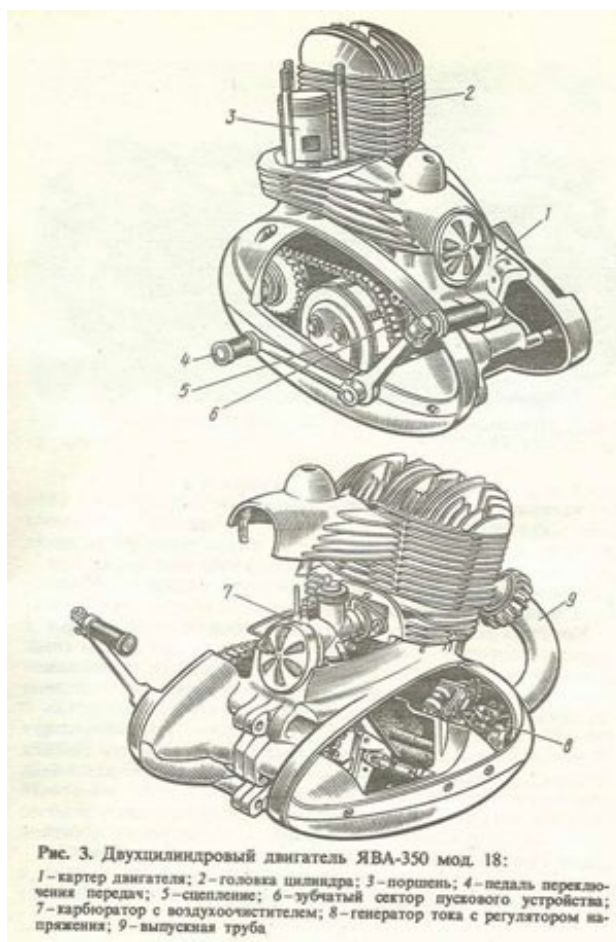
Двухцилиндровый двигатель ЯВА-350 мод. 18:
